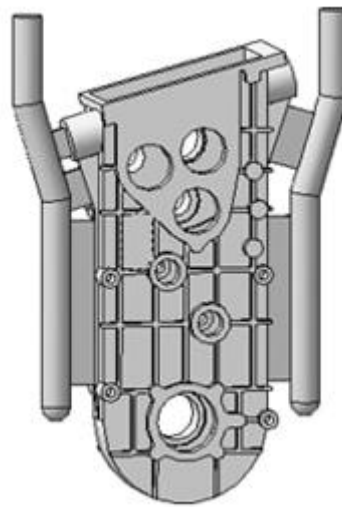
Вилівка «Корпус коробки передач з ЛПС»
